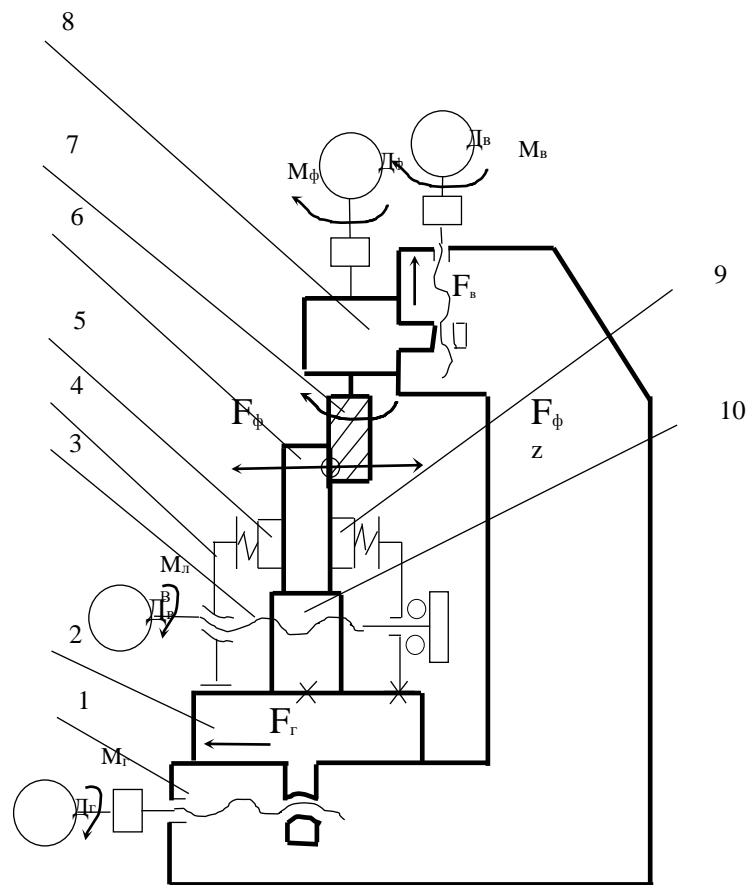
Спрощена схема фрезерного верстата з лещатами: 1-верстат; 2-робочий стіл; 3-гвинтова пара приводу затиску; 4-лещата; 5,9-затискні елементи-губки; 6-об'єкт затиску-деталь; 7-фреза; 8-шпиндельна бабка; 10-упор для деталі
